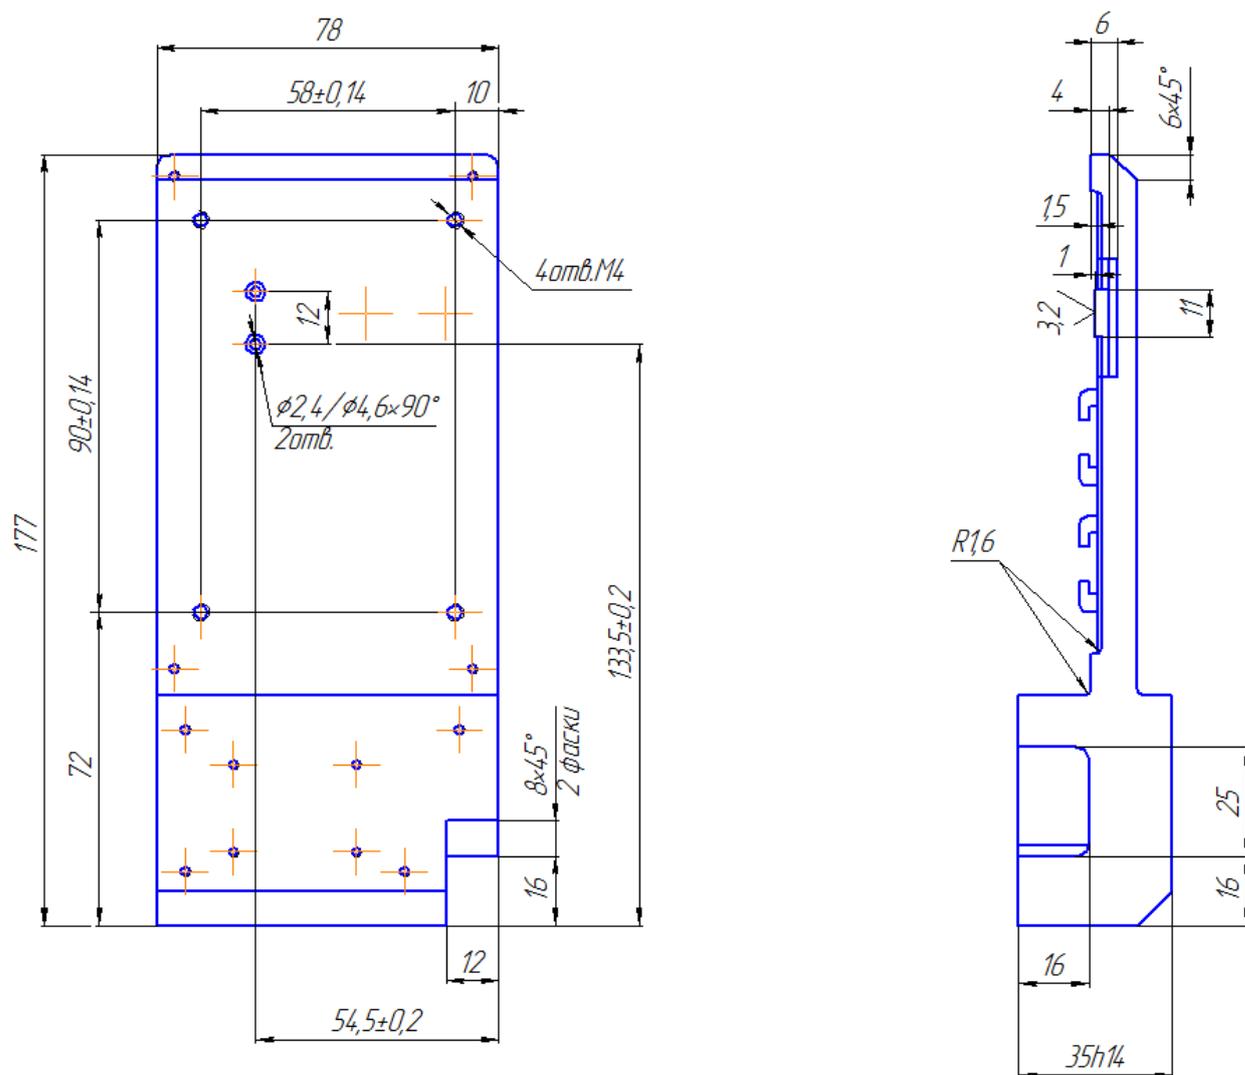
Эскиз корпуса координатно-измерительной машины Mora Primus
